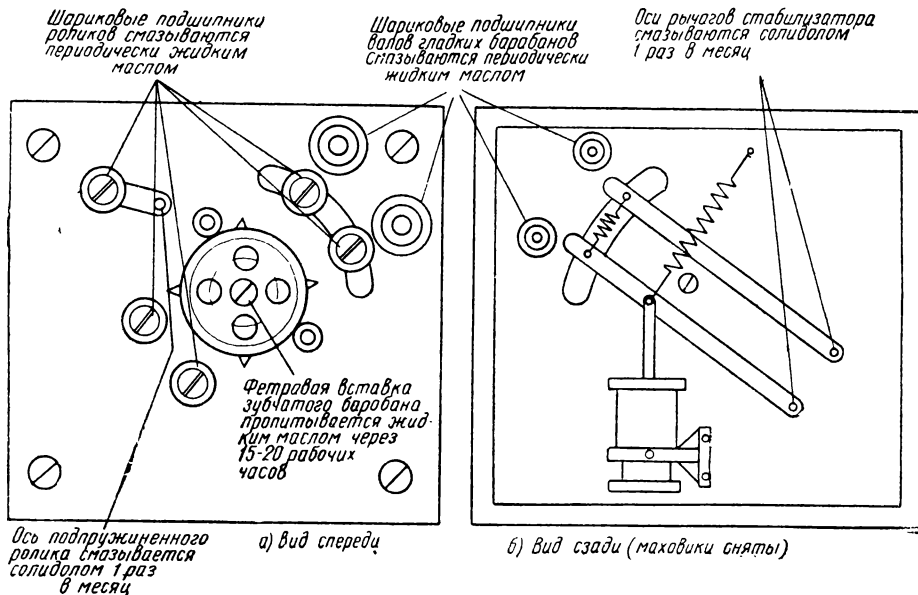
Местная смазка магнитной звуковой приставки кинопроектора КПТ-3
